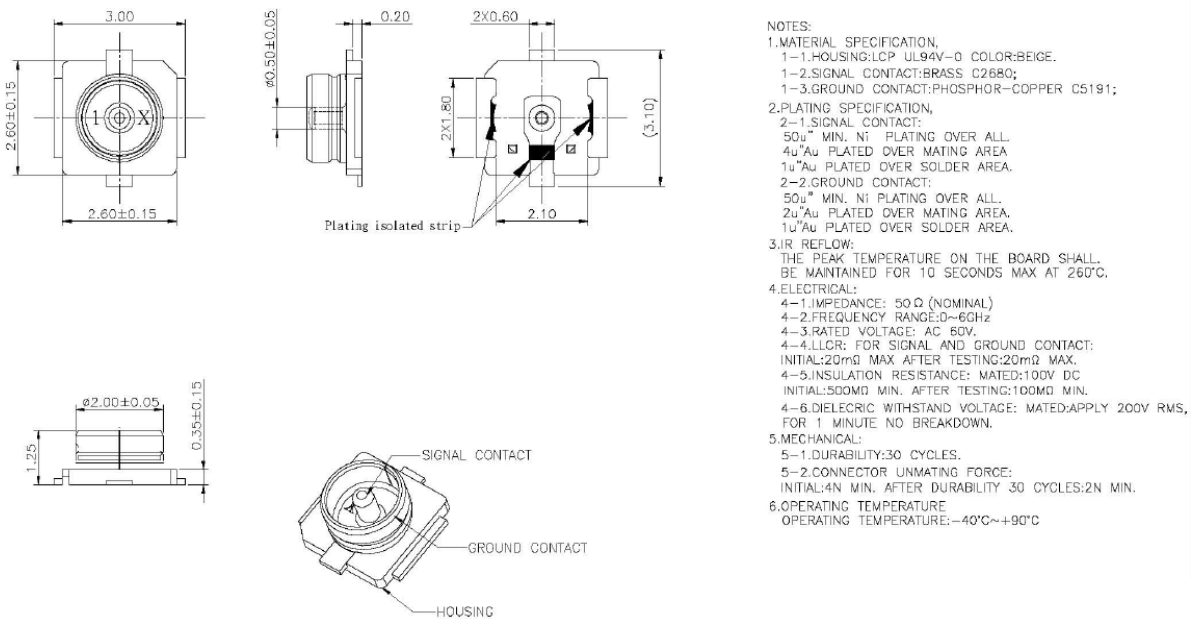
1代 IPEX 焊盘尺寸
